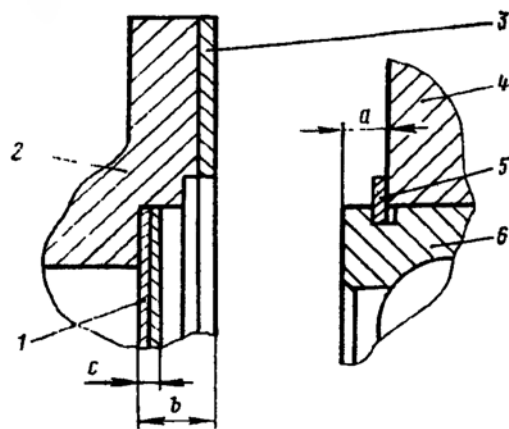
Схема заусов для регулирования осевых зазоров в подшипниках ведущего и ведомого валов:
